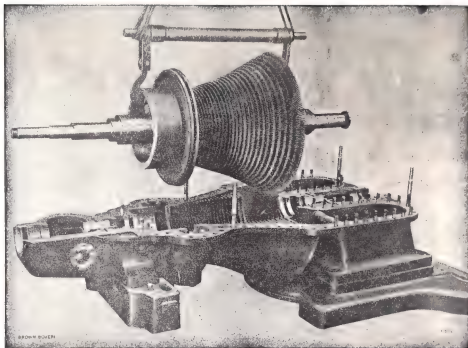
Rotor de una turbina combinada de acción y reacción.
